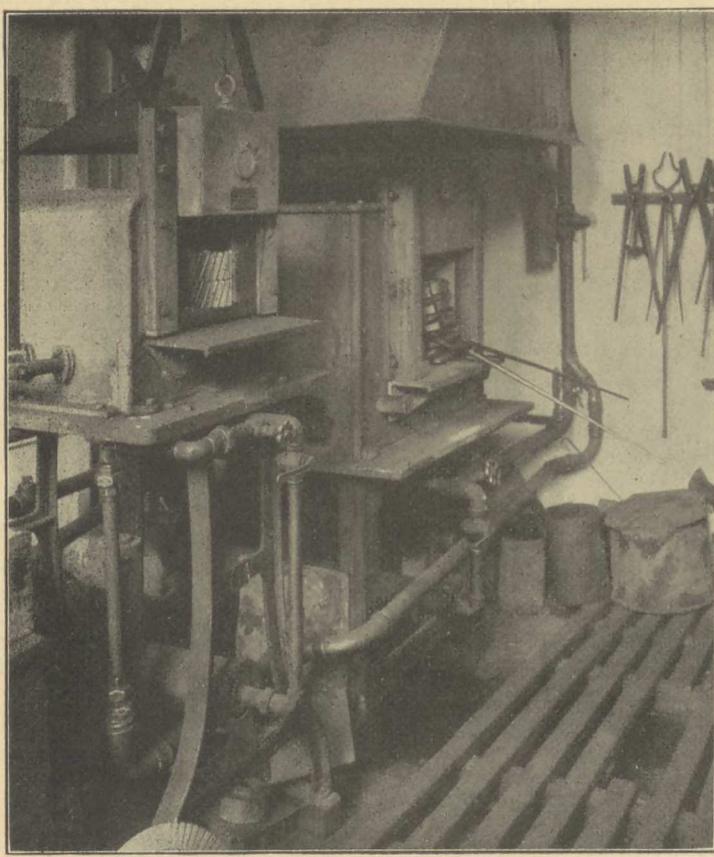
Gasglühofen zum Härteln von Zahnräderfräsern.
